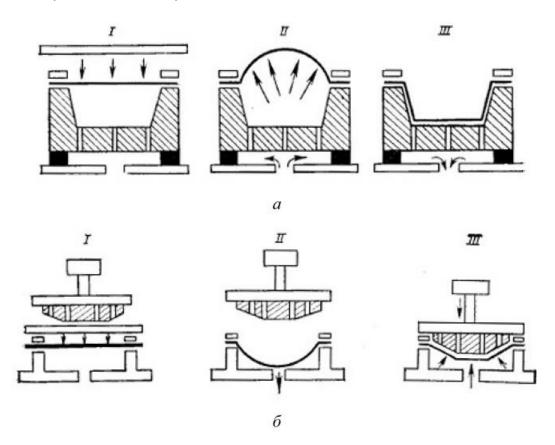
Формование с пневматической вытяжкой: а – негативное; б – позитивное
